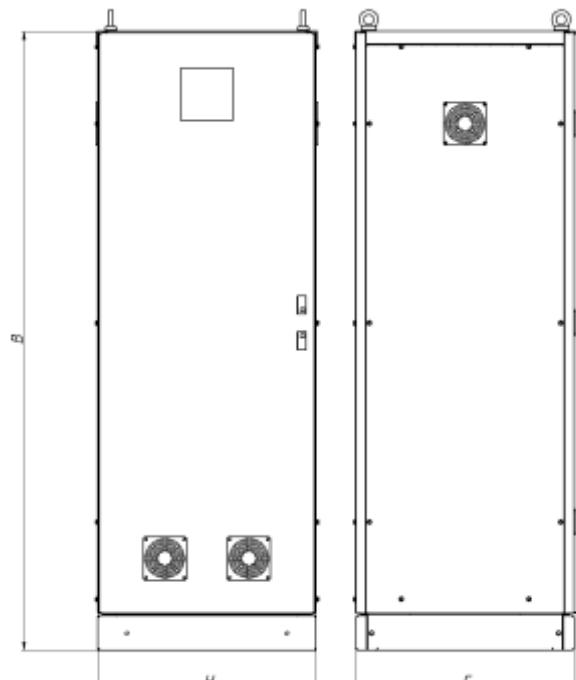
Габаритный чертеж установок ВАРНЕТ-АС
